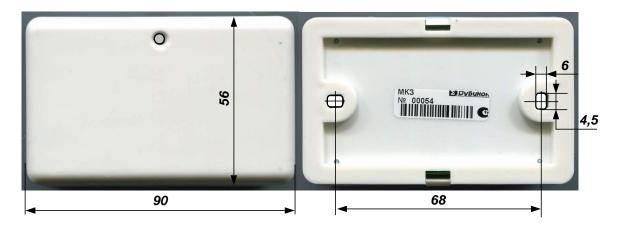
Габаритные и присоединительные размеры корпуса МКЗ
